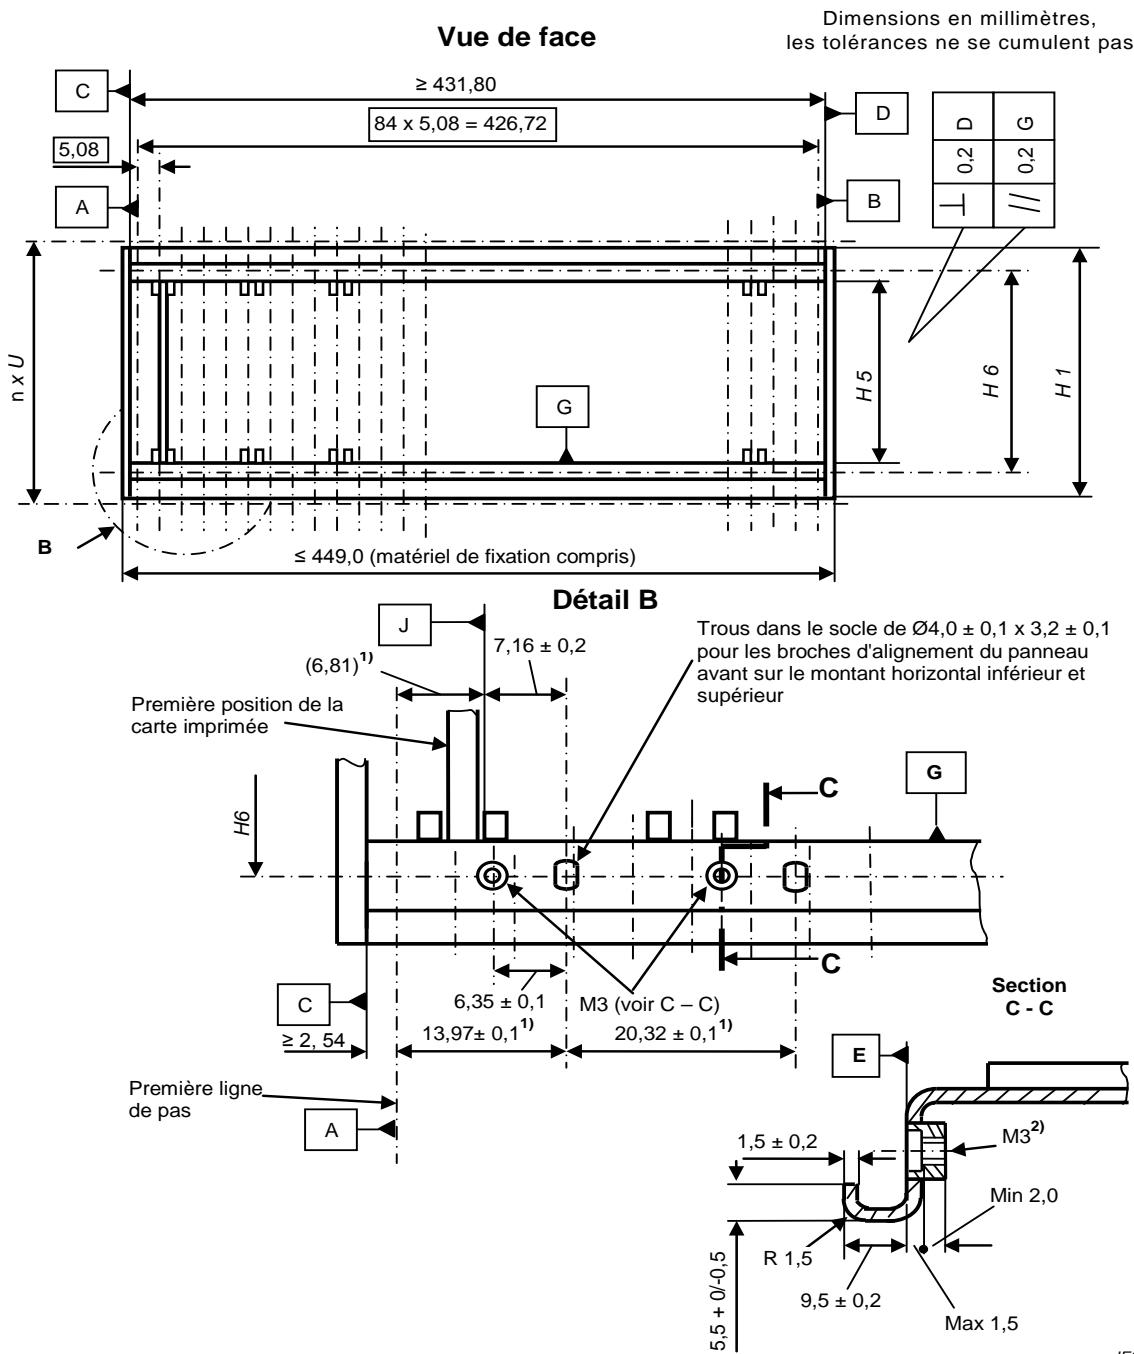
Dimensions de montage arrière d'un bac de type RA
